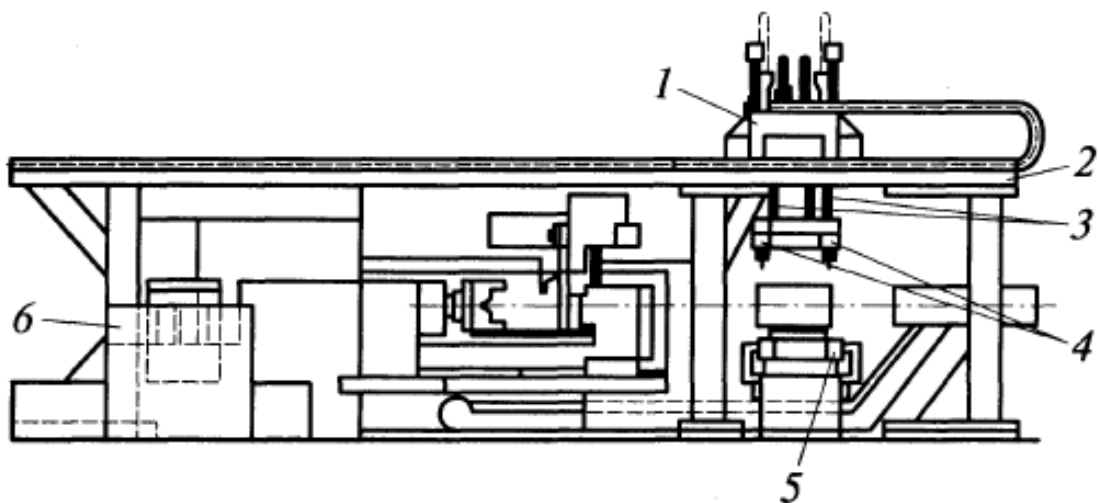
ГПМ на базе токарного станка с фронтальным расположением рабочего органа робота:
